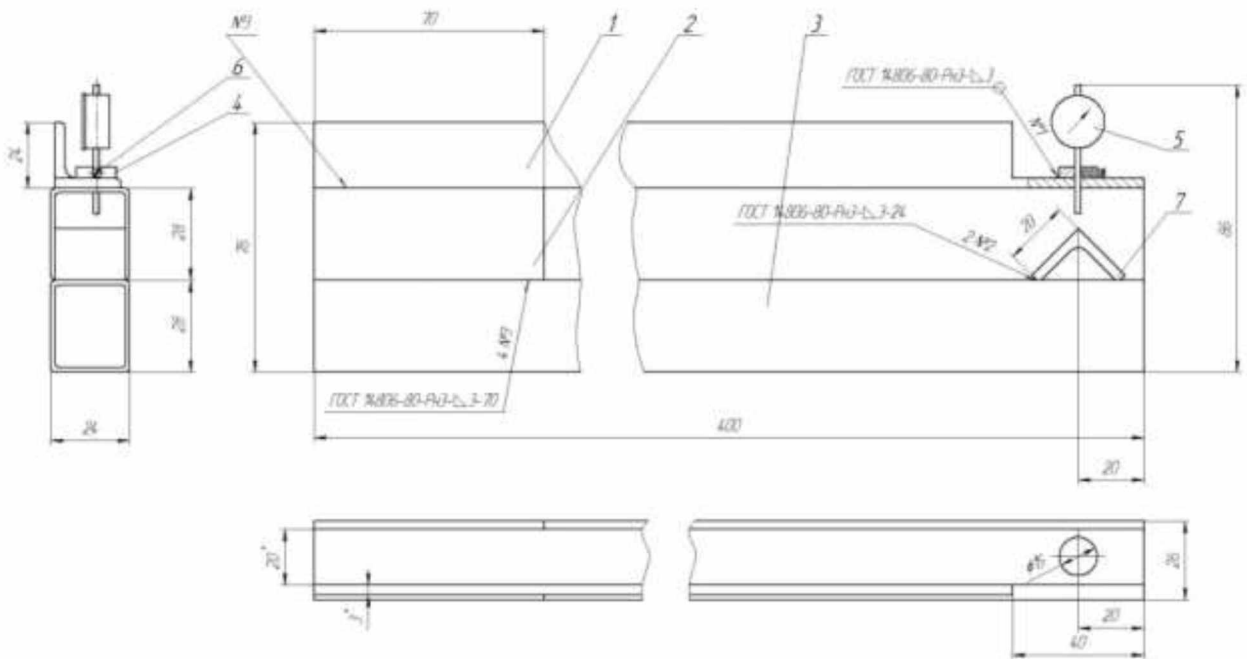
Креслення пристосування для вимірювання зносу
